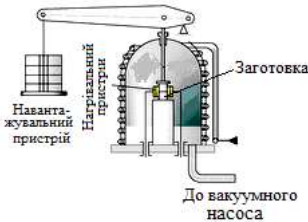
Схема дифузійного зварювання у вакуумі
